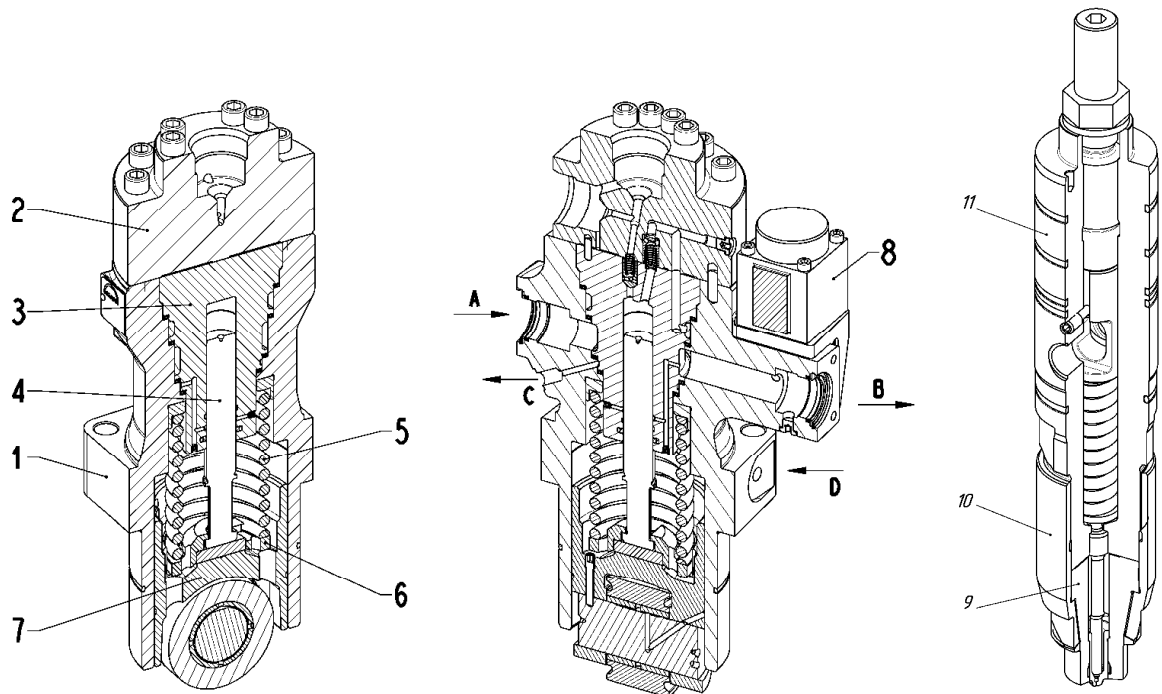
Паливний насос високого тиску та форсунка: 1 – корпус ПНВТ; 2 – кришка; 3 – втулка; 4 – плунжер; 5 – пружина; 6 – регулювальна прокладка; 7 – штовхач; 8 – клапан керування; 9 – розпилювач; 10 – накидний стакан; 11 – корпус форсунки
